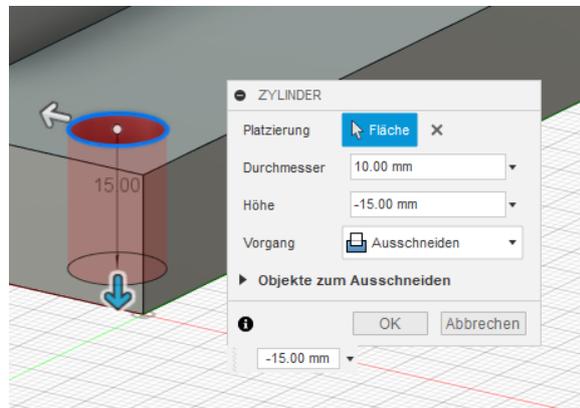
Erstellen einer Bohrung mit Werkzeug ZYLINDER
